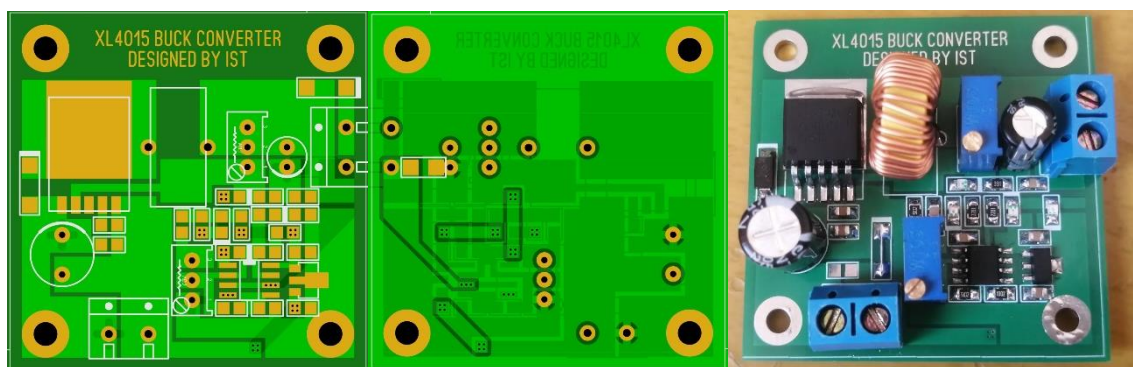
锂电池恒压恒流充电管理 PCB 设计图与实物装配图
